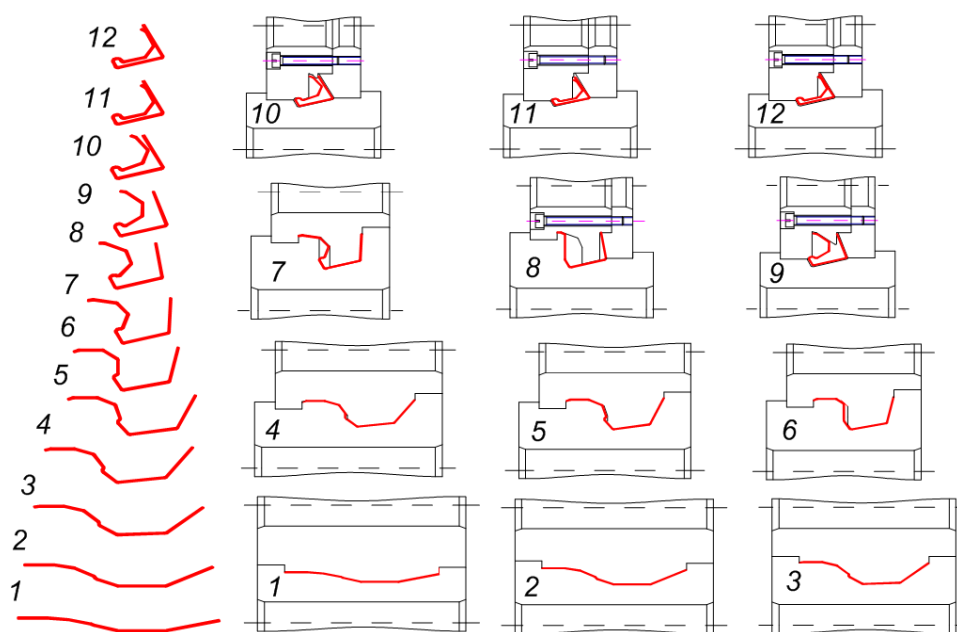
Схема формовки и валковые калибры профиля 29×32×9×0,7 мм
